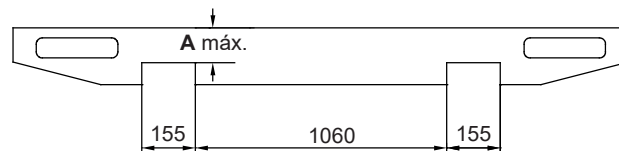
ZL-45-90, ZL-75-90, ZL-45-110, ZL-75-110
